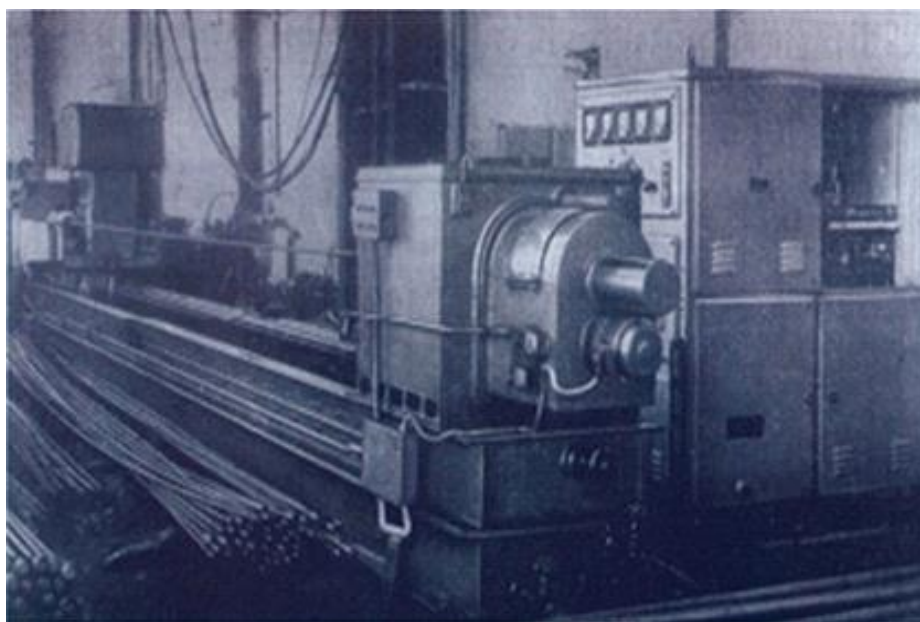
Одно ручейный станок для поверхностной закалки готовых насосных штанг
